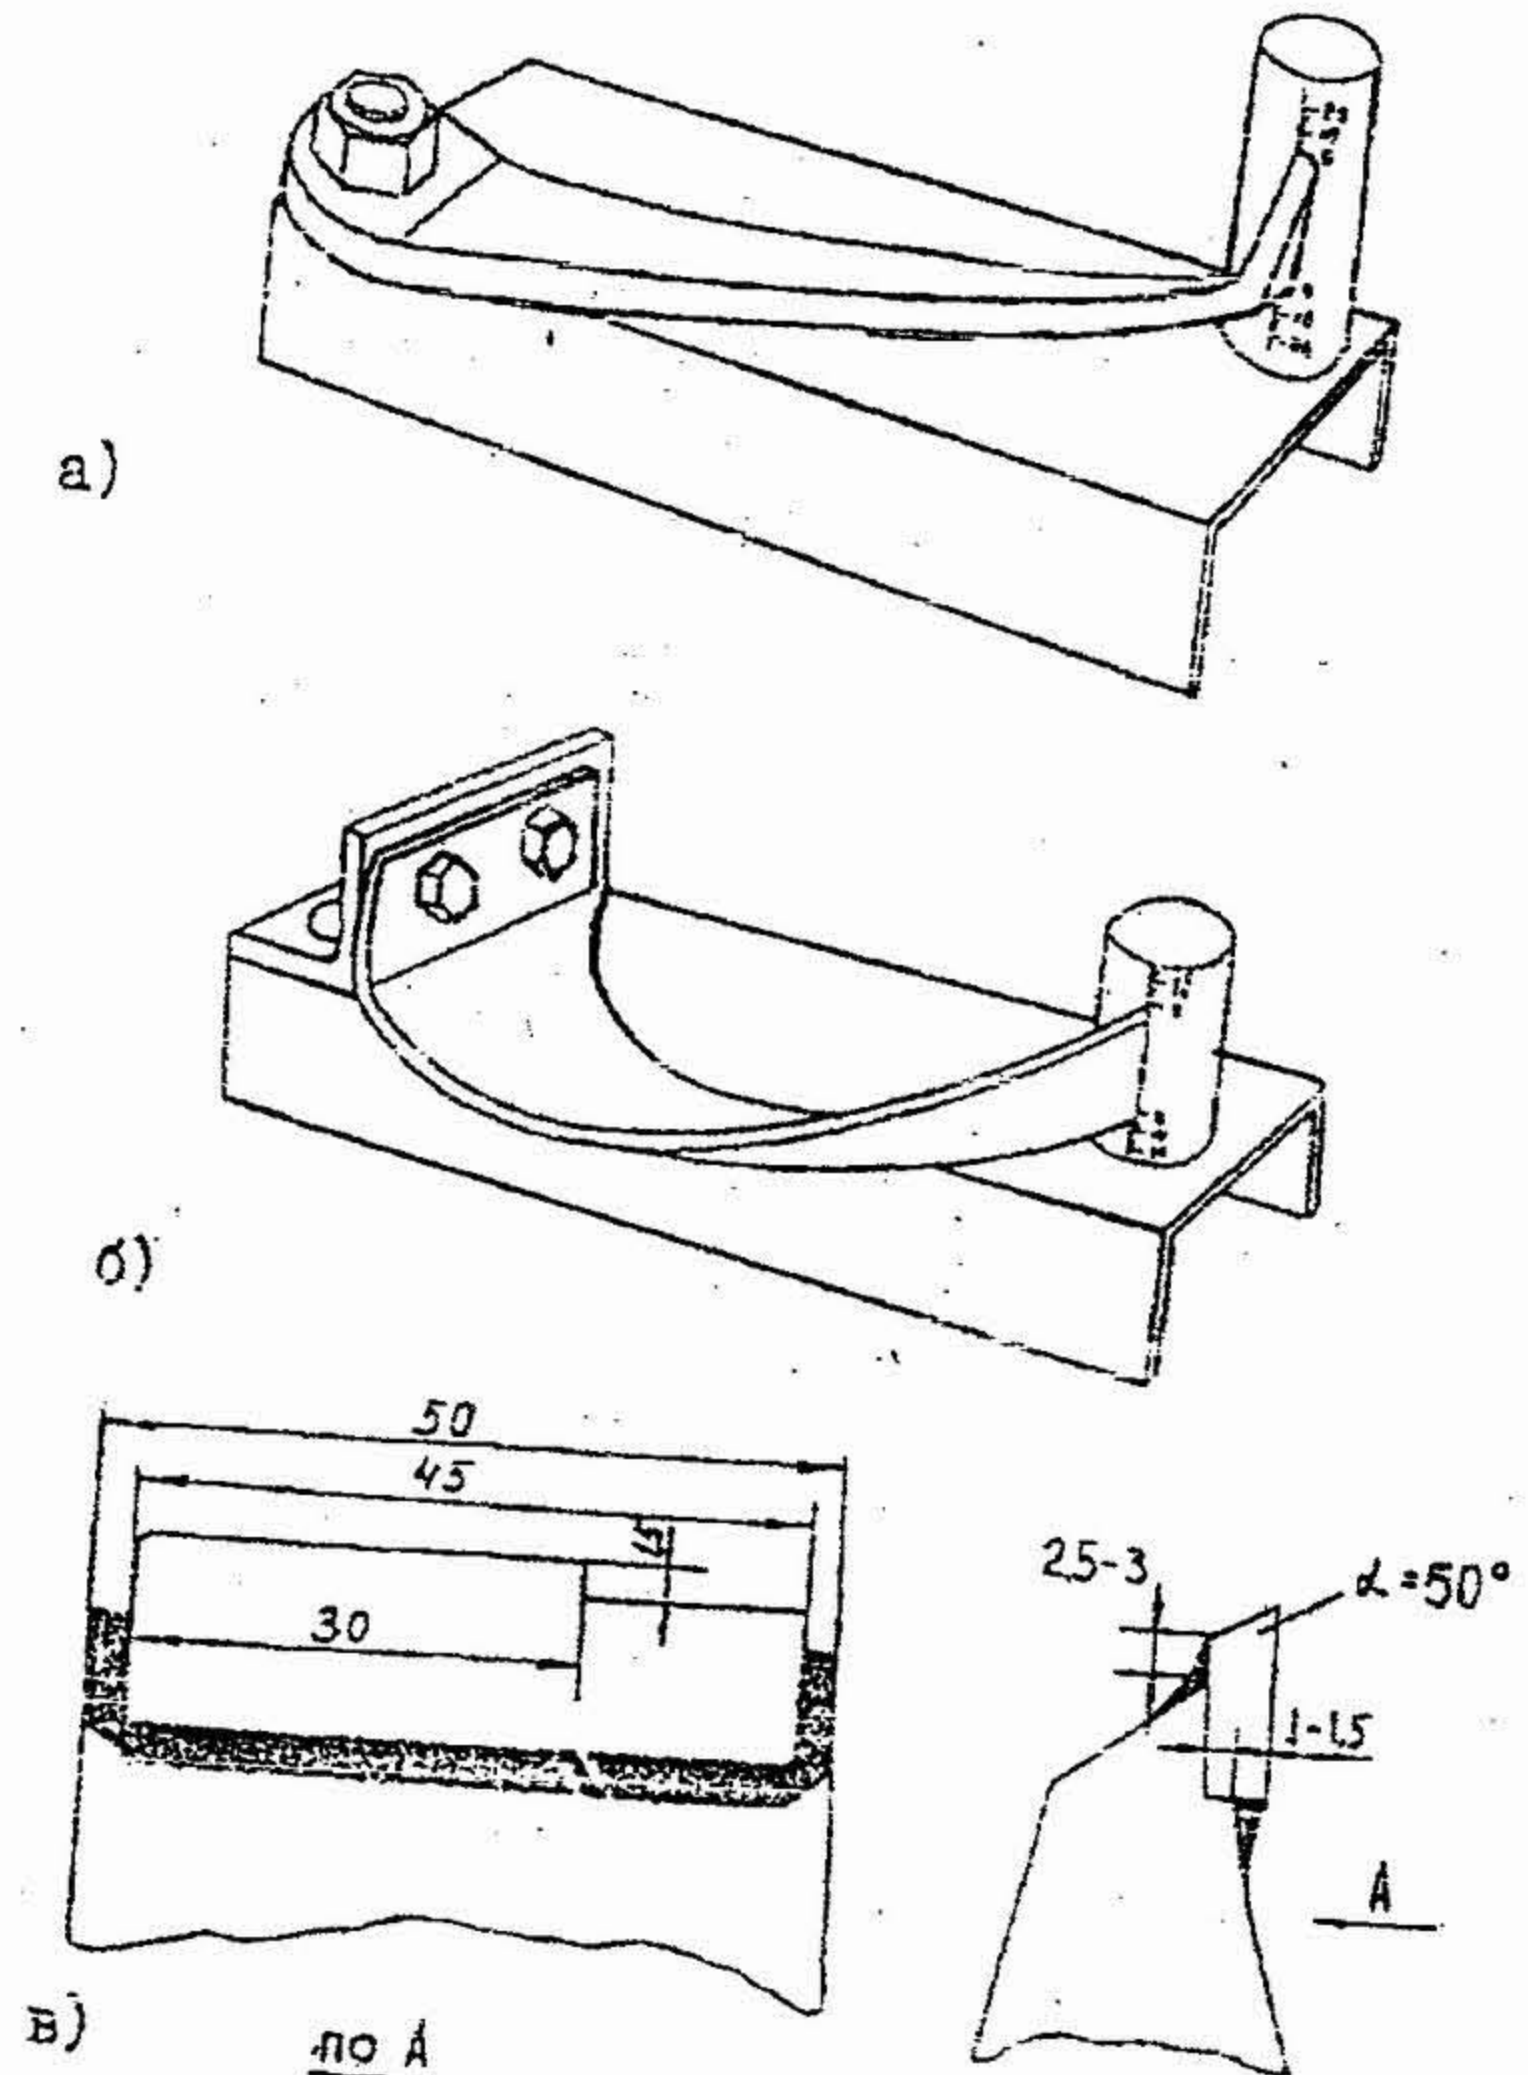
Общий вид короснимателей в шаблонах для контроля параллельности рабочей кромки оси бревна, длины, положения передних точек рабочих кромок, углов:
